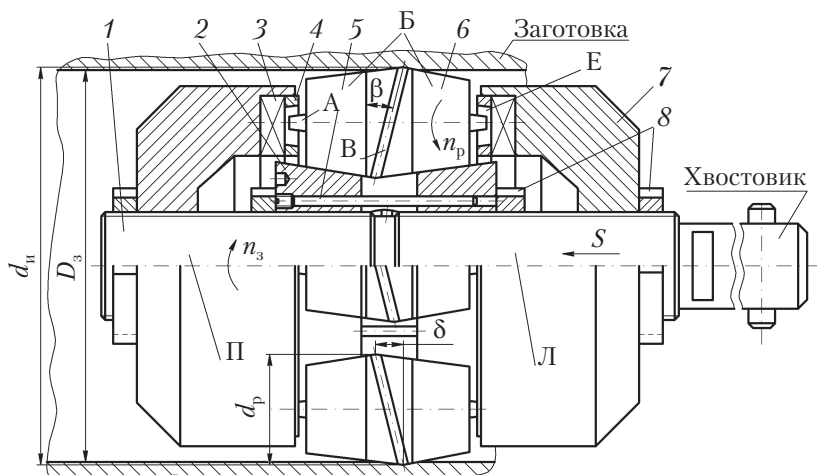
Многороликное устройство для виброраскатывания отверстий
